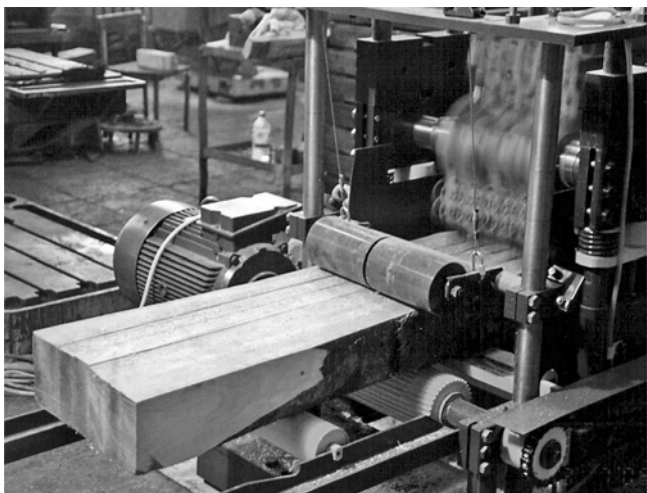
Распиловка бруса на опытном станке с круговым поступательным движением полотен
